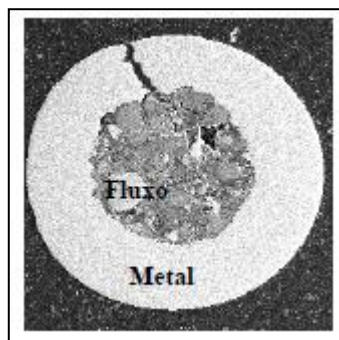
Seção transversal de um arame tubular SAW (Modenesi e Marques – Soldagem I - 2006)
